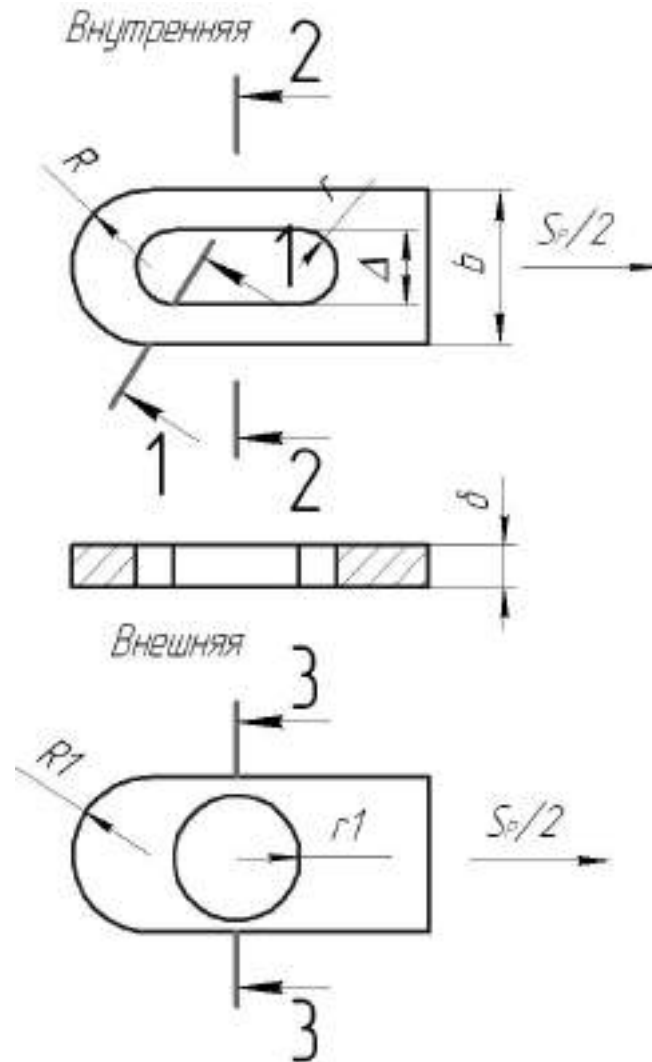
Розрахункова схема для перевірного розрахунку пластини
